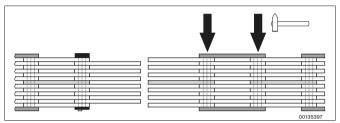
Kürzen: Schweißnaht sprengen
